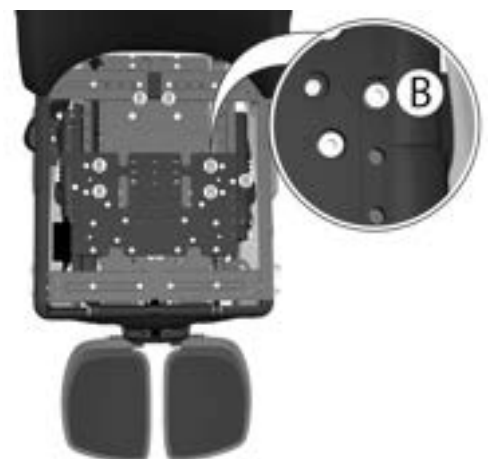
Die Position des hinteren Abschnitts des Sitzrahmens (Rückenlehnenposition) wird mit sieben Schrauben gehalten, die hier mit dem Buchstaben B markiert sind.
